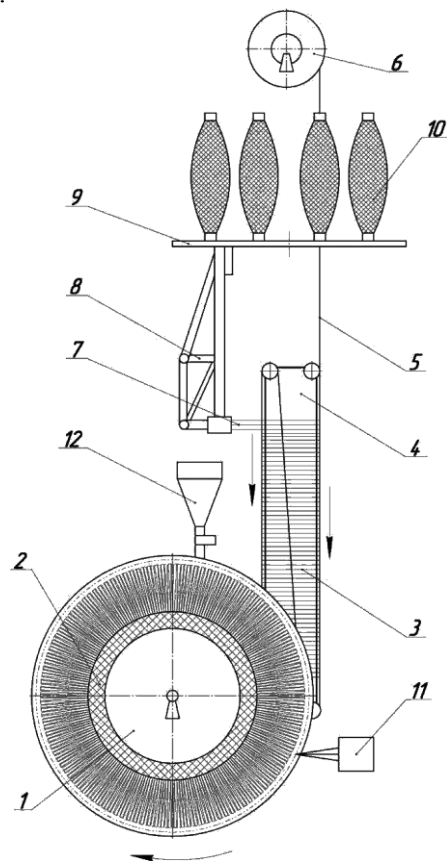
Схема изготовления ворсового нетканого изделия
